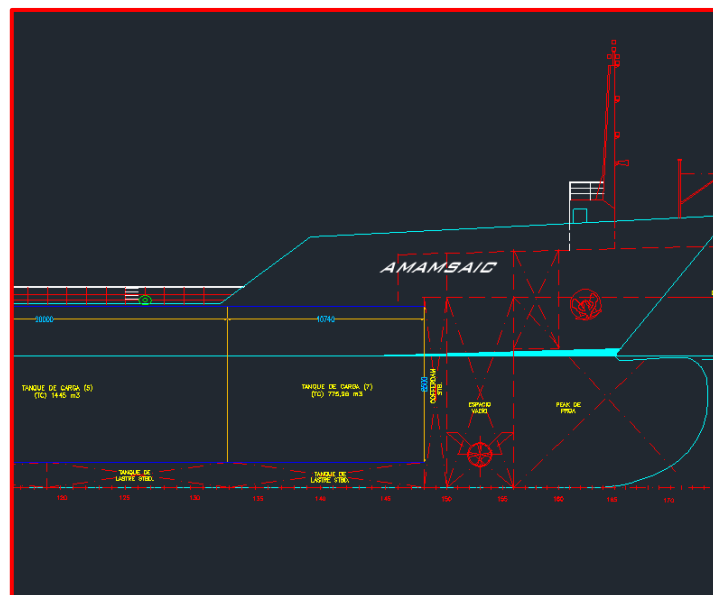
Disposición tanques de carga (Alzado, zona de estribor)
